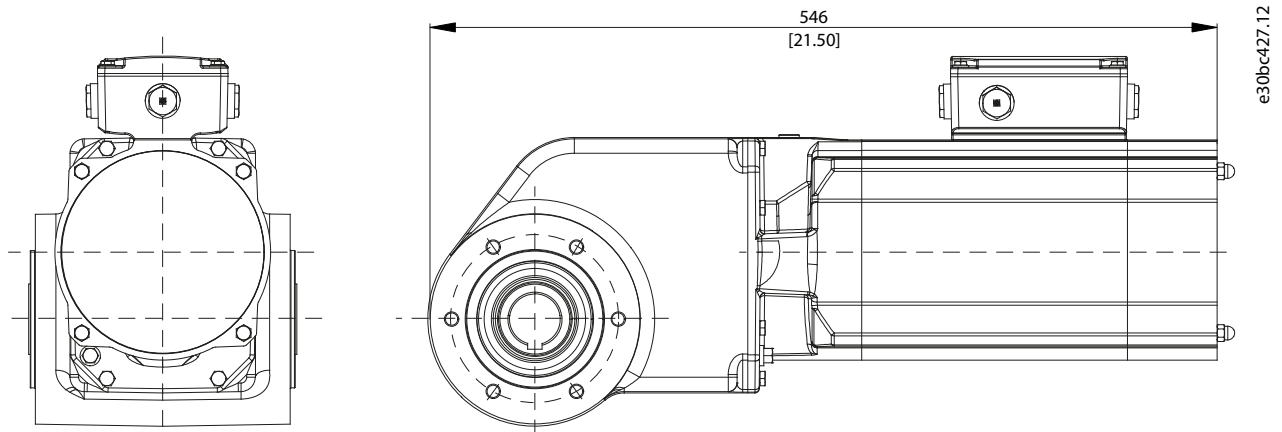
Dimensioni del VLT® OneGearDrive® con opzione freno meccanico
